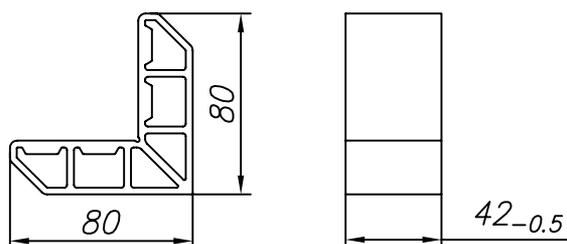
Изготовление соединителя углового FLGU.400.0914
